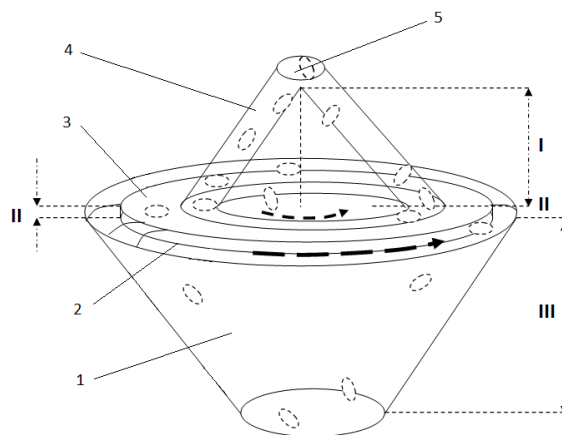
Схема корпуса скарификатора с указанием рабочих органов: 1 – приемник (бункер), 2 – вращающийся диск (ротор), 3 – неподвижный диск (крышка), 4 – вращающийся конус, 5 – семяпровод.
